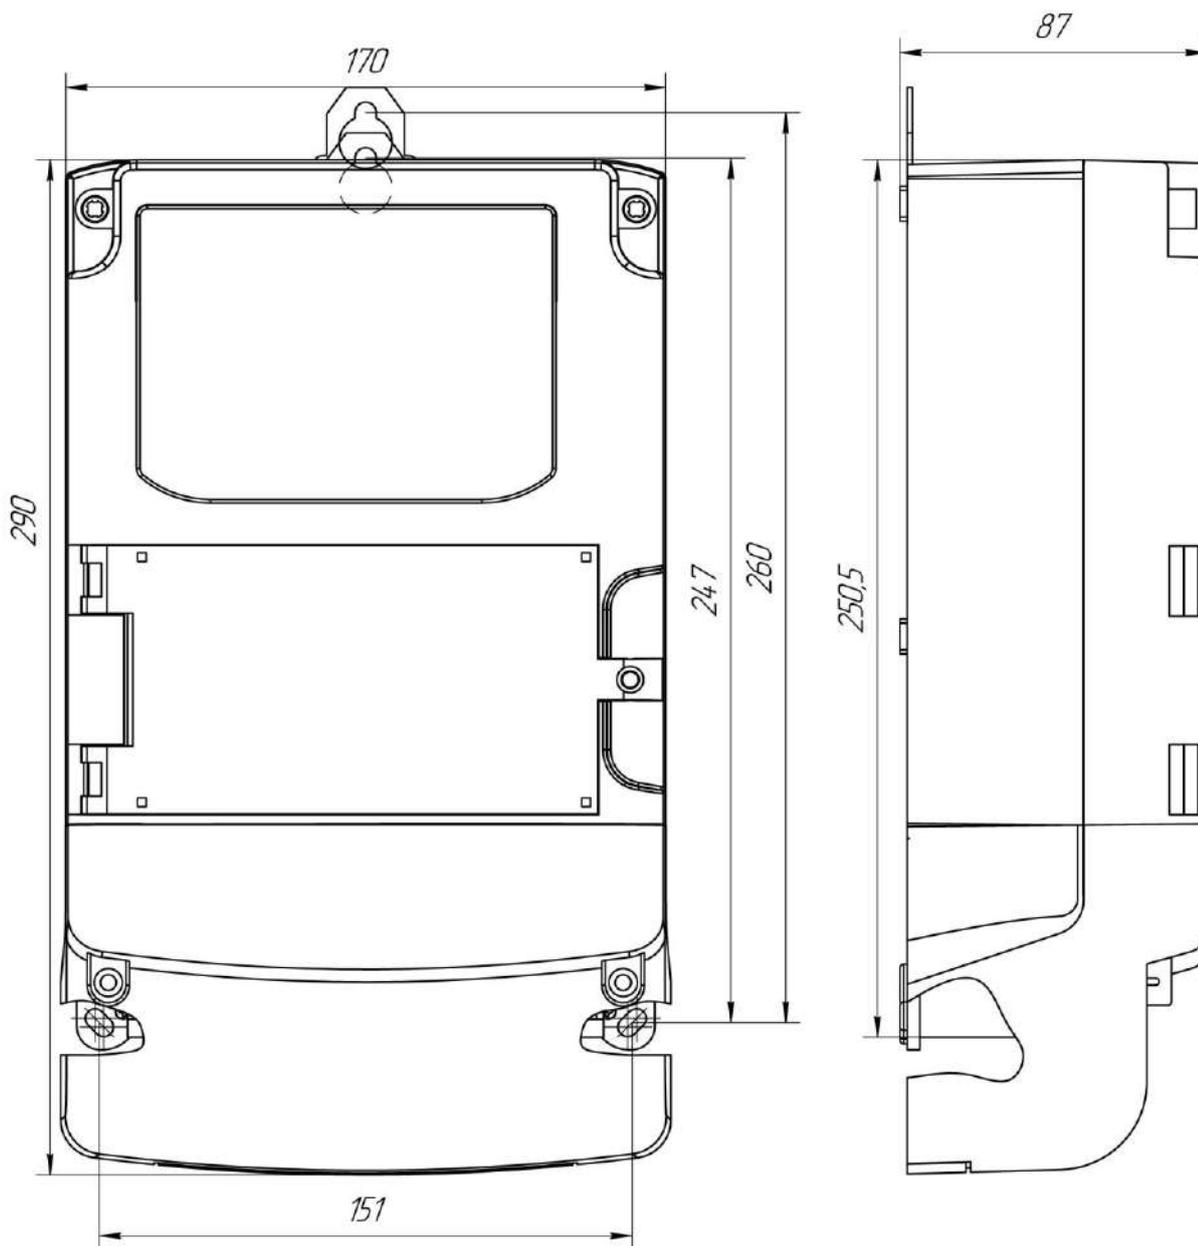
Габаритные и установочные размеры счетчика
